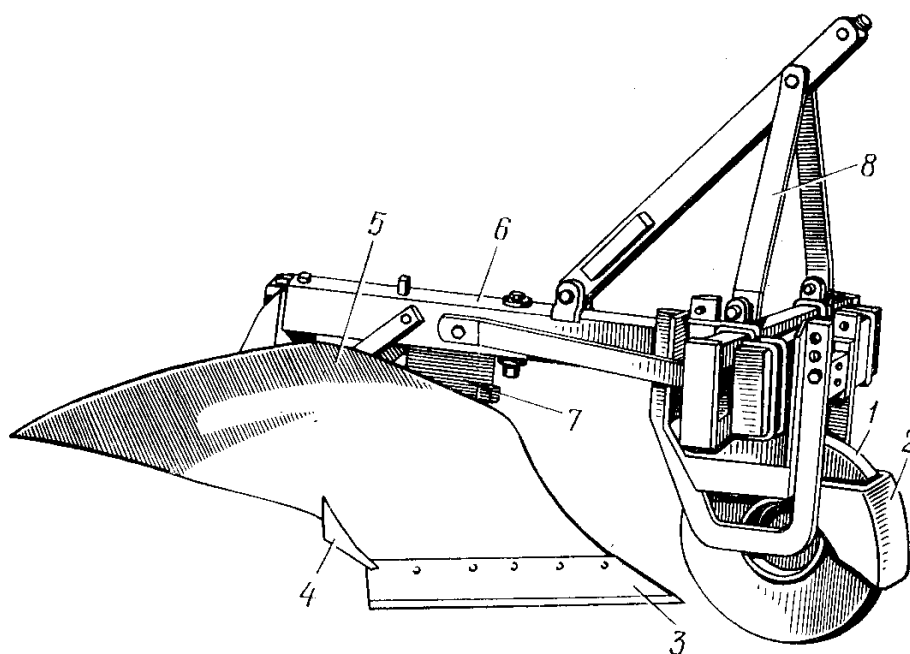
Плуг ПКЛ-70 (с одноотвальным корпусом): 1- дисковый нож; 2- защитный лобовик; 3 - лемех; 4 — боковой подрезной нож 5 — отвал; 6 — рама; 7 — стойка; 8 — устройство для навески
